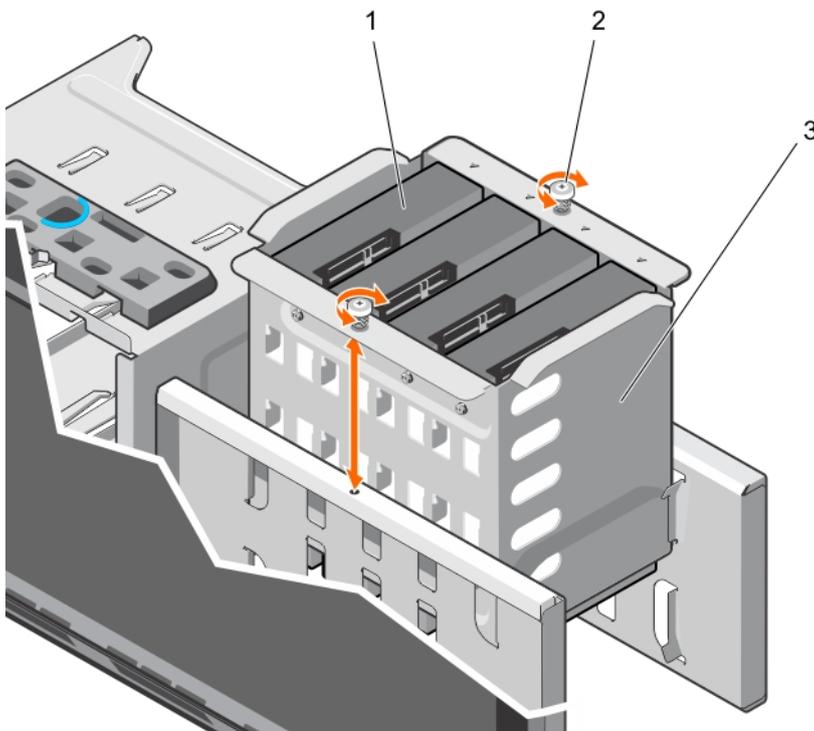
Installieren und Entfernen des internen Festplattenlaufwerkschachts
